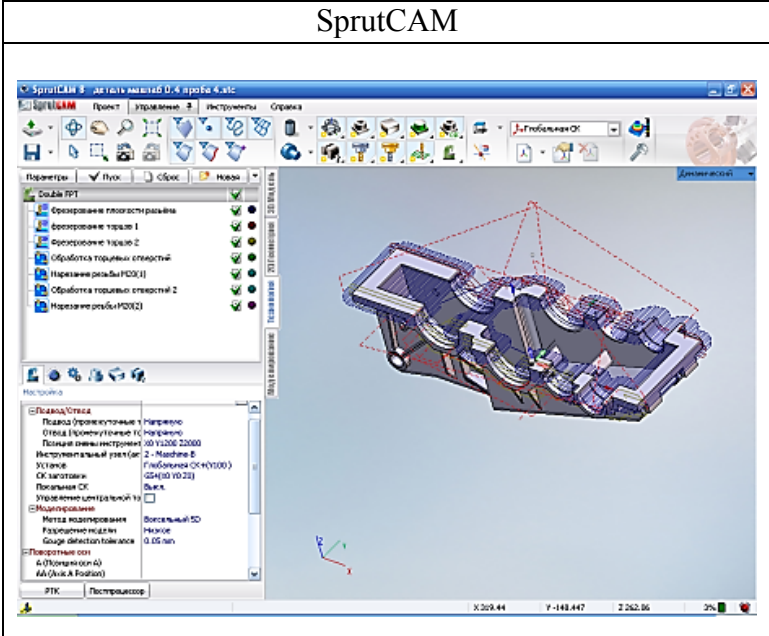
Корпус редуктора ЦЗ-900 эскалатора метро ЕТК-245
